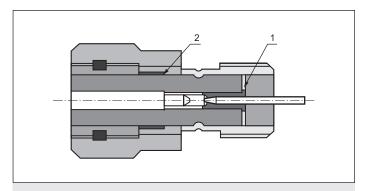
Соединители в сочлененном состоянии: 1 — розетка СРГ50-751ФВ; 2 — вилка СР-50-726ФВ
